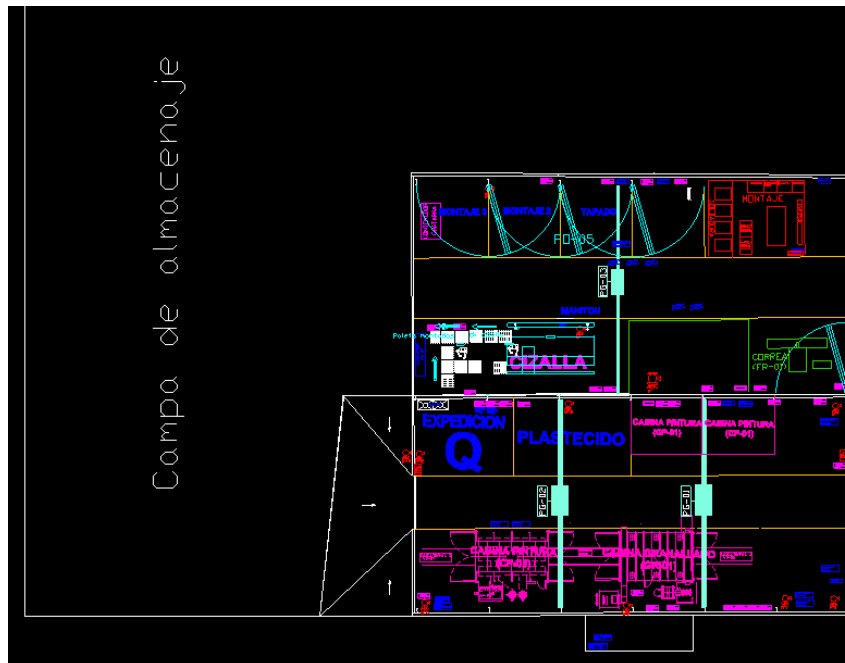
zona de la nave donde se colocarían las instalaciones
